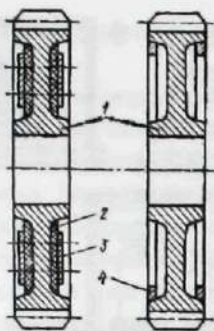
Способы борьбы с шумом колес зубчатых передач
